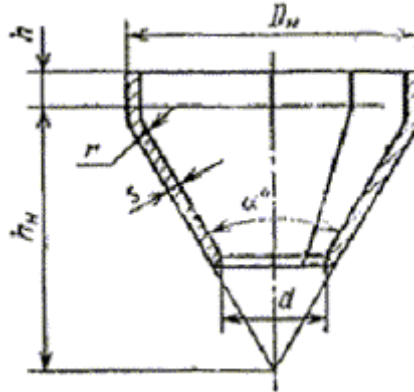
Розрахункова схема корпусу сушарки
